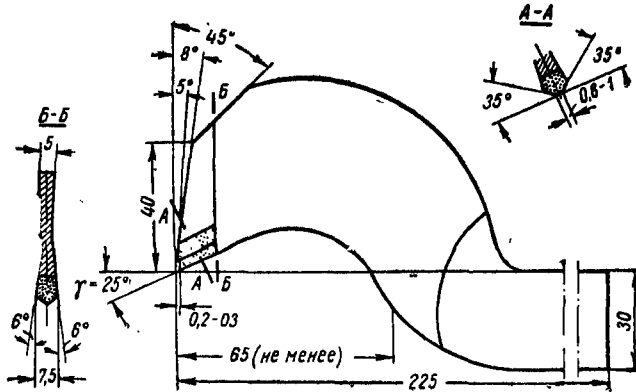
Жесткий отрезной резец конструкции В. Я. Карасева.
